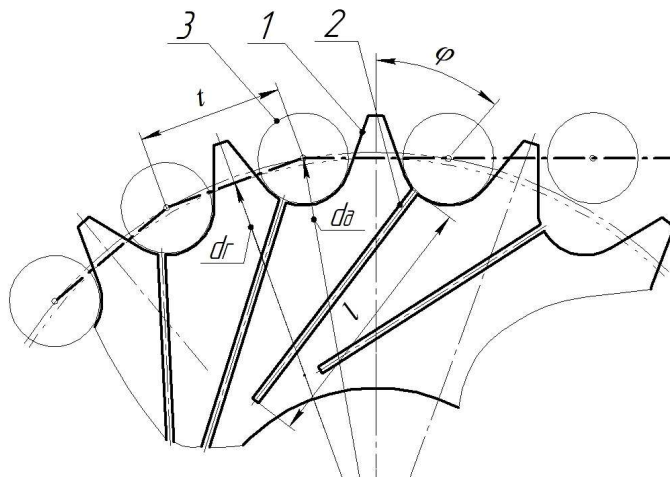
Звездочка с консольными зубьями, образованными косыми прорезями
